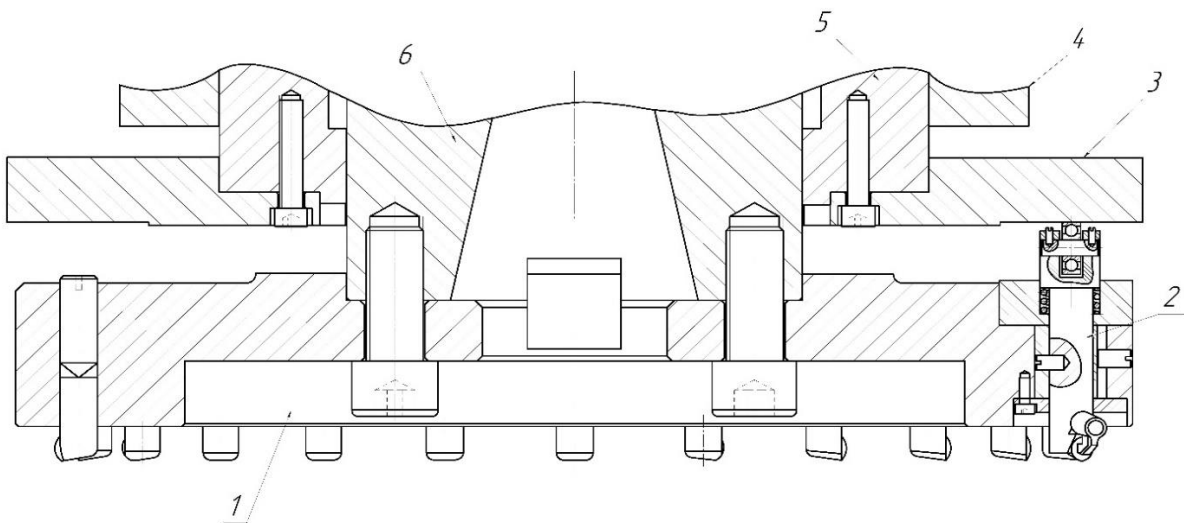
Конструкція фрези з рухомих різальним елементом (1 – корпус фрези; 2 – рухомий різальний елемент; 3 – копір; 4 – верстат; 5 – нерухома частина верстата; 6 – шпиндель)
